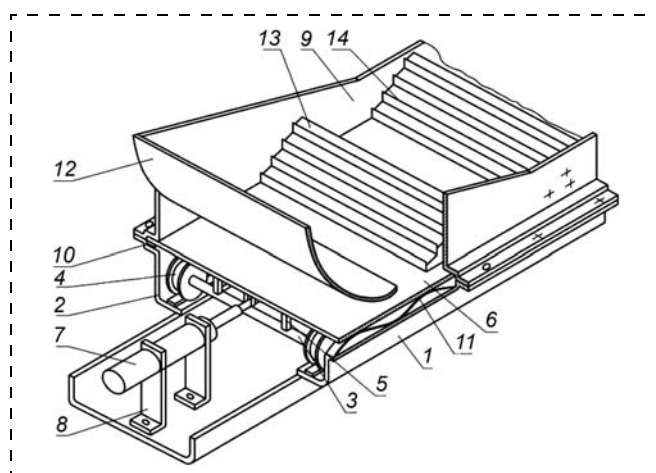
Конструкция клинового перегружателя грузонесущего типа: 1 — базовая рама; 2 — направляющие; 3 — ось; 4 — катки; 5 — штанги; 6 — днище; 7 — гидроцилиндр; 8 — опора; 9 — борт; 10 — пазы базовой рамы; 11 — пластинчатая пружина; 12 — бункер; 13 — транспортирующий клиновой элемент; 14 — стопорный клиновой элемент
